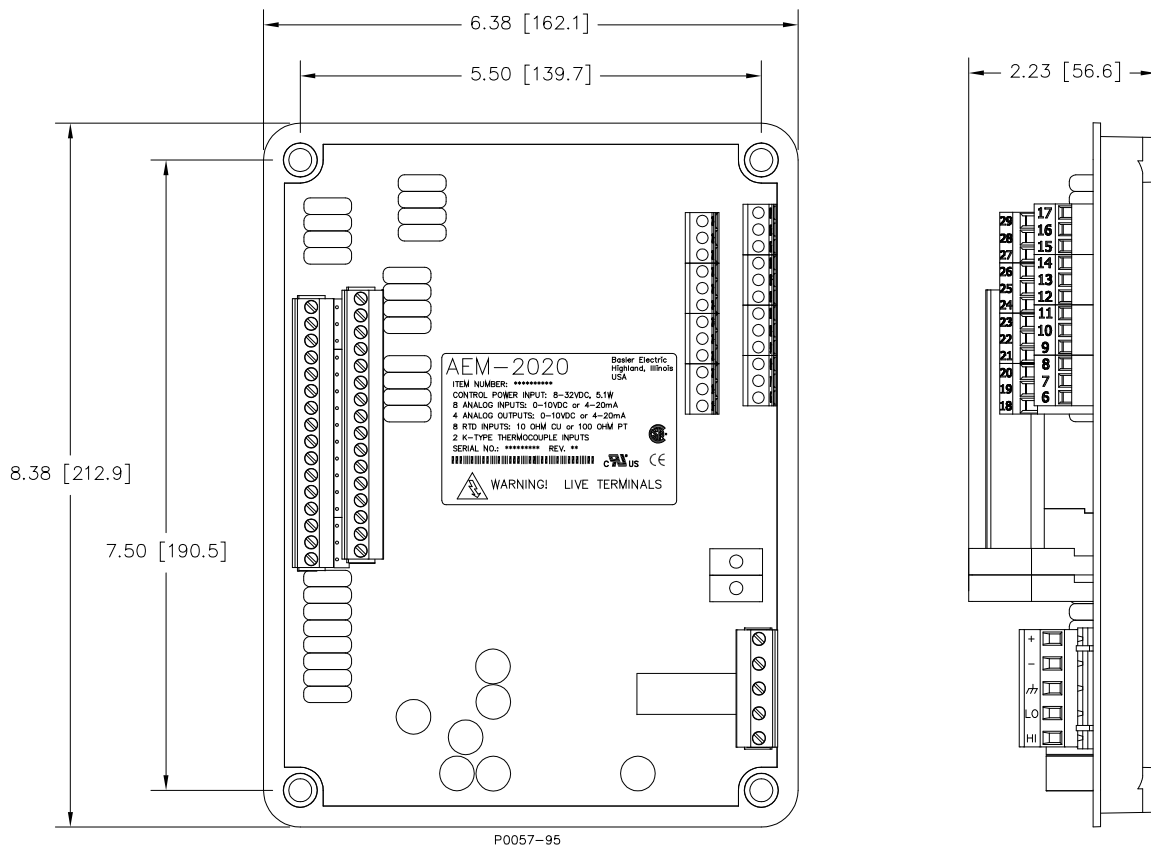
Dimensions générales hors-tout du module AEM-2020
